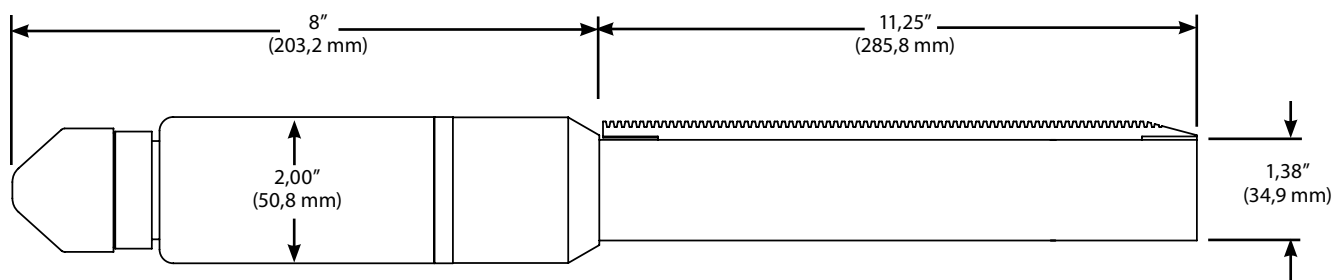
Dimensions de la torche en ligne PT-26 « SL »
